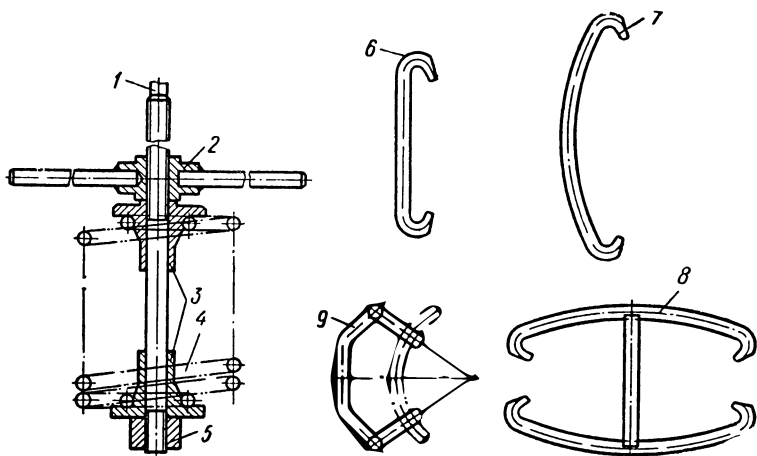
Приспособление для снятия и установки пружин откидывания кабины автомобиля ГАЗ-66:
